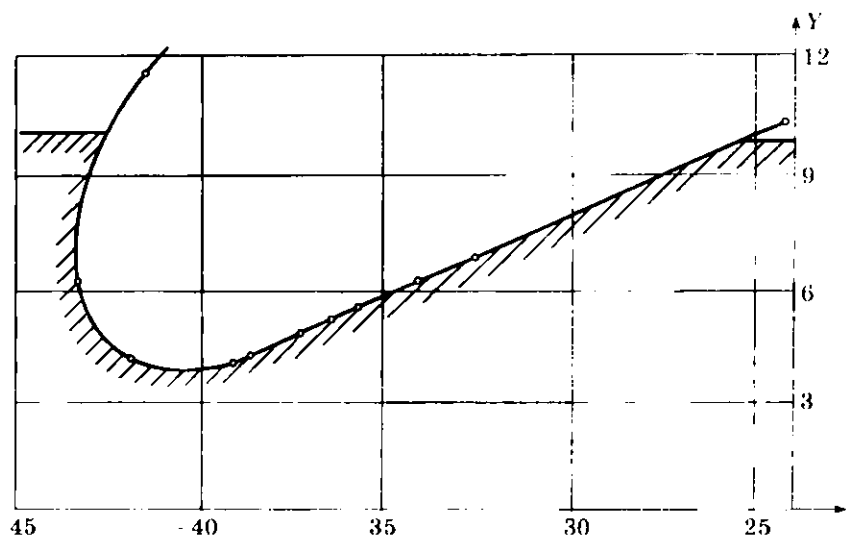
Расчетный профиль осевого сечения канавки шнекового сверла после обработки угловой фрезы
